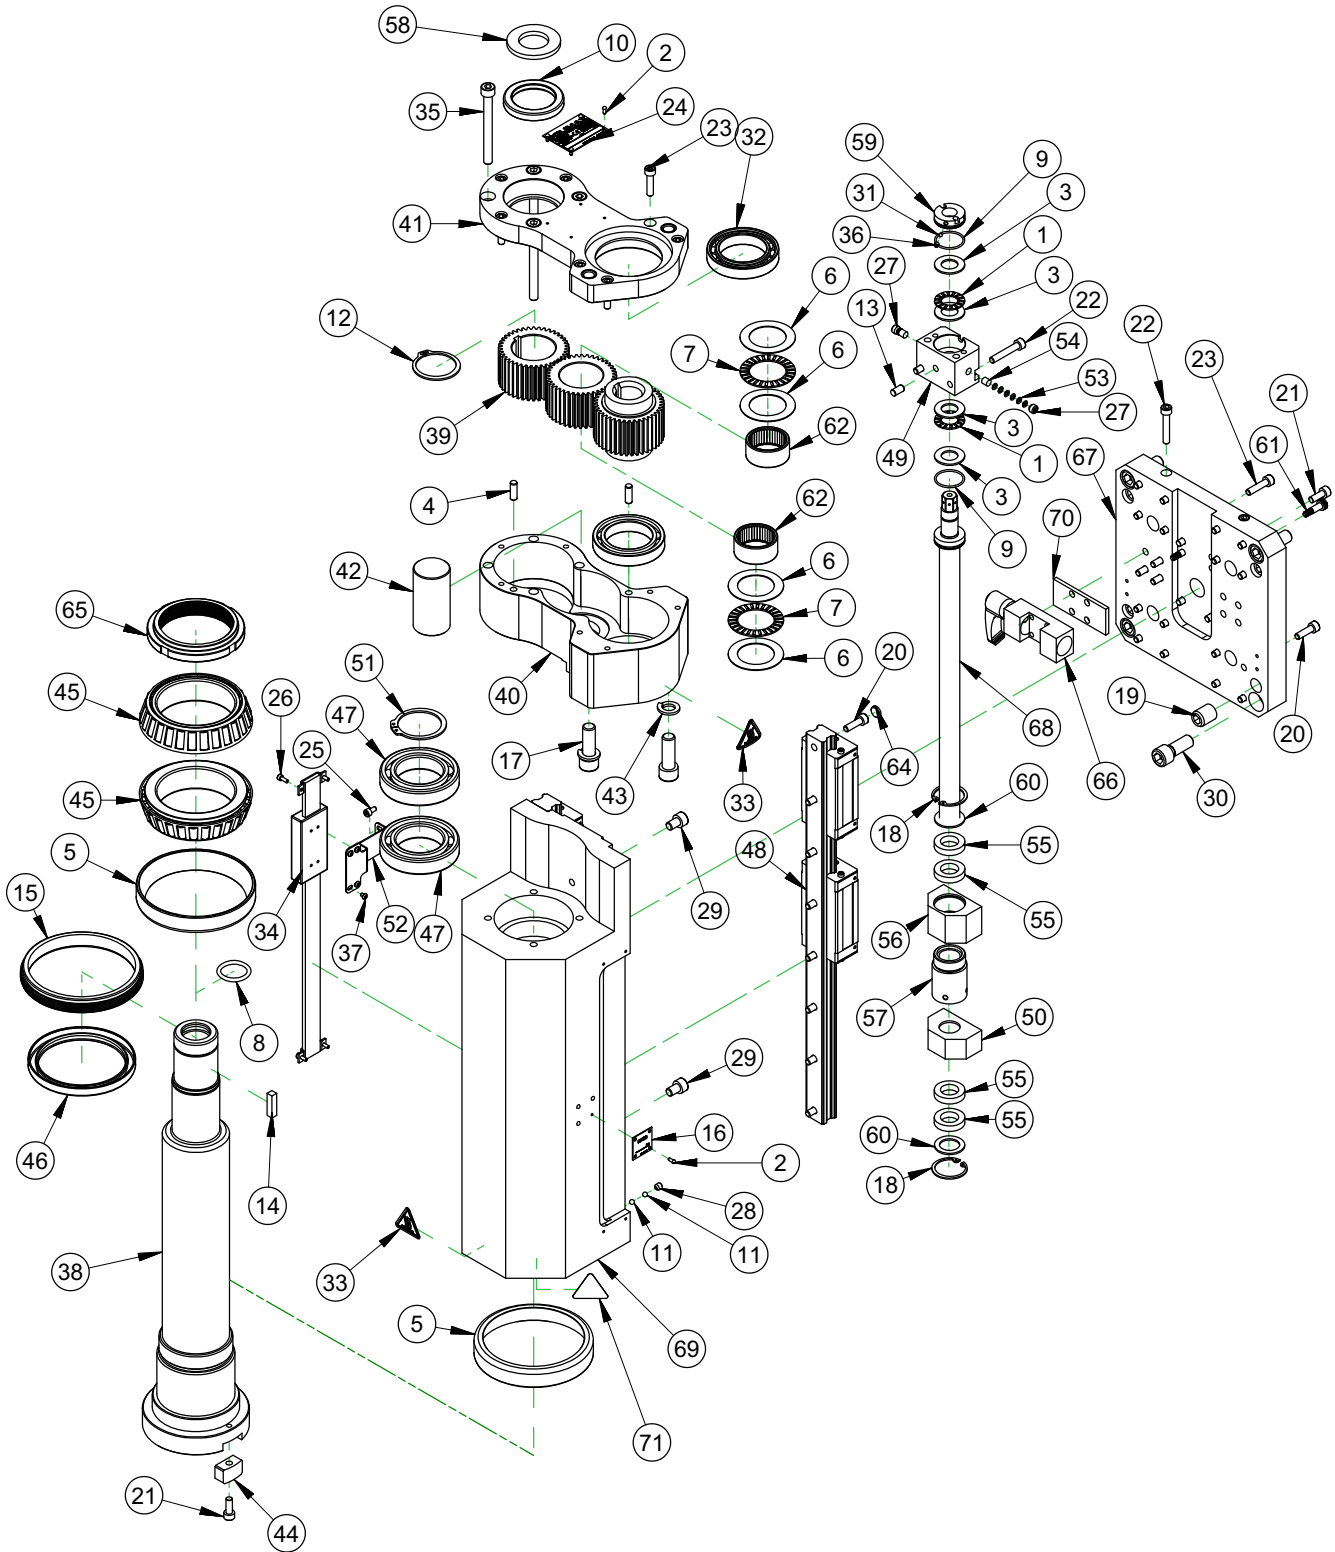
TÊTE DE FRAISAGE 2-29/32 PAL. COURSE 8 CÔNE #50 (P/N 72277)
